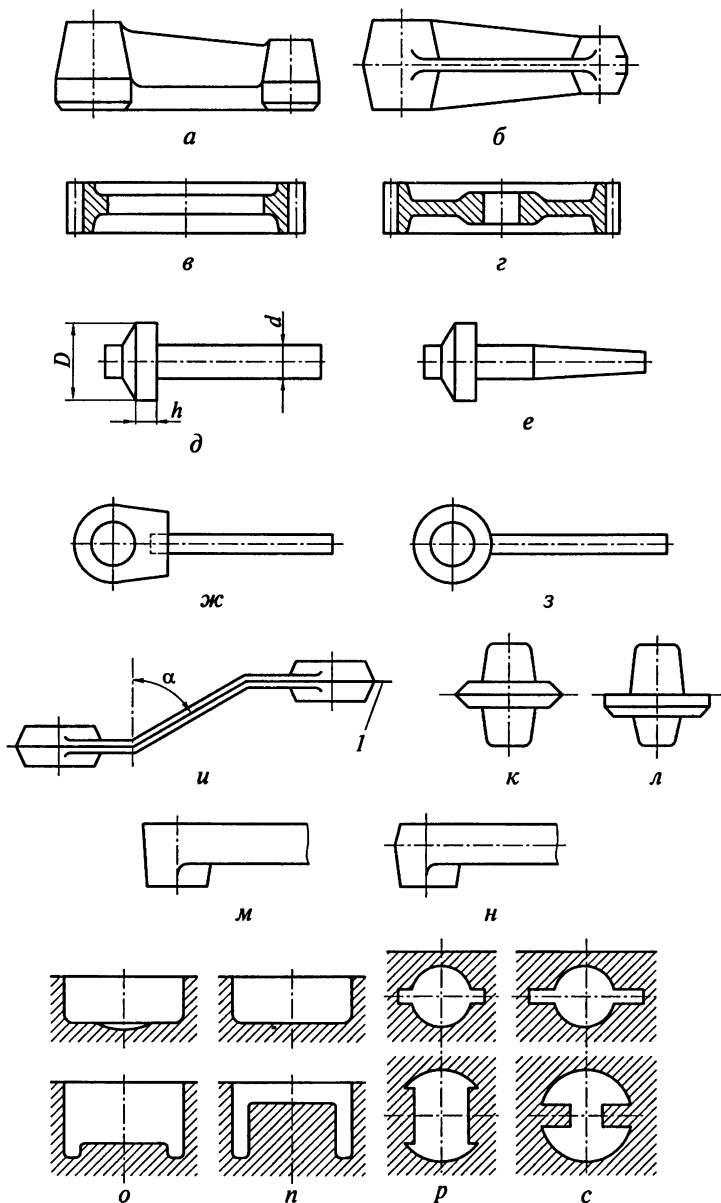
Примеры технологичных (*а, в, д, ж, к, м, о, р*) и нетехнологичных (*б, г, е, з, л, н, п, с*) конструкций заготовок, получаемых штамповкой; *и* — ломаная поверхность разреза:
